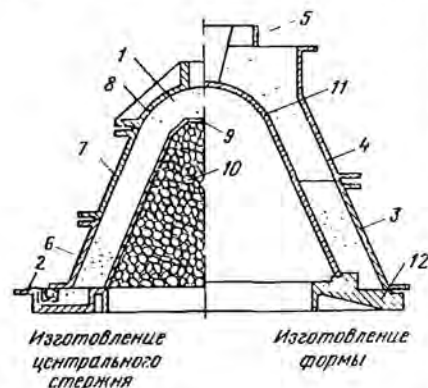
Схема оснастки для изготовления стержня и формы чаши шлаковоза
